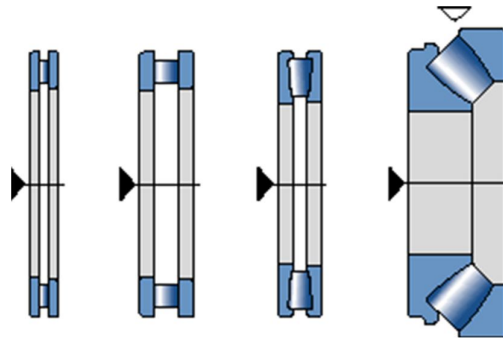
12.- Rodamientos axiales de bolas con contacto angular
